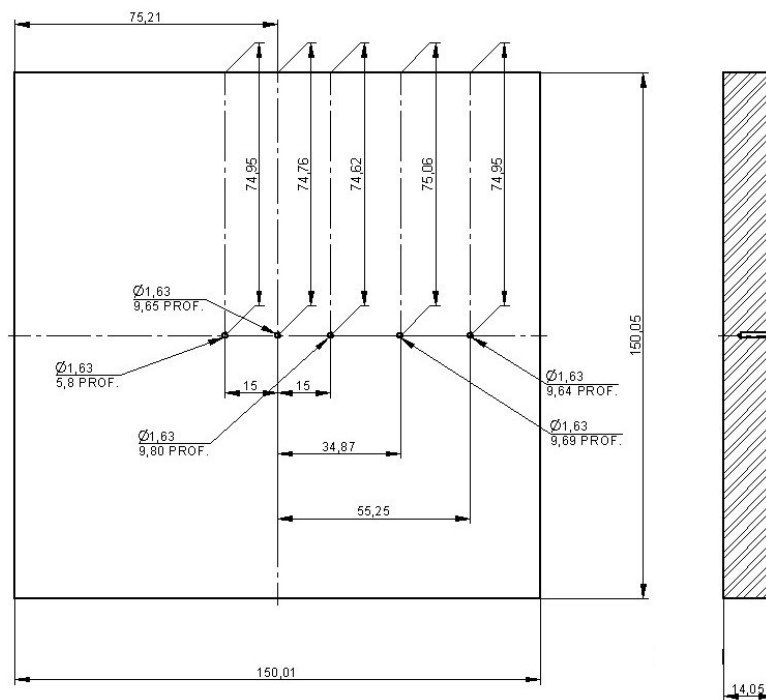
Resultado da aferição dimensional da placa 05, mostrando as dimensões reais após a fabricação.
